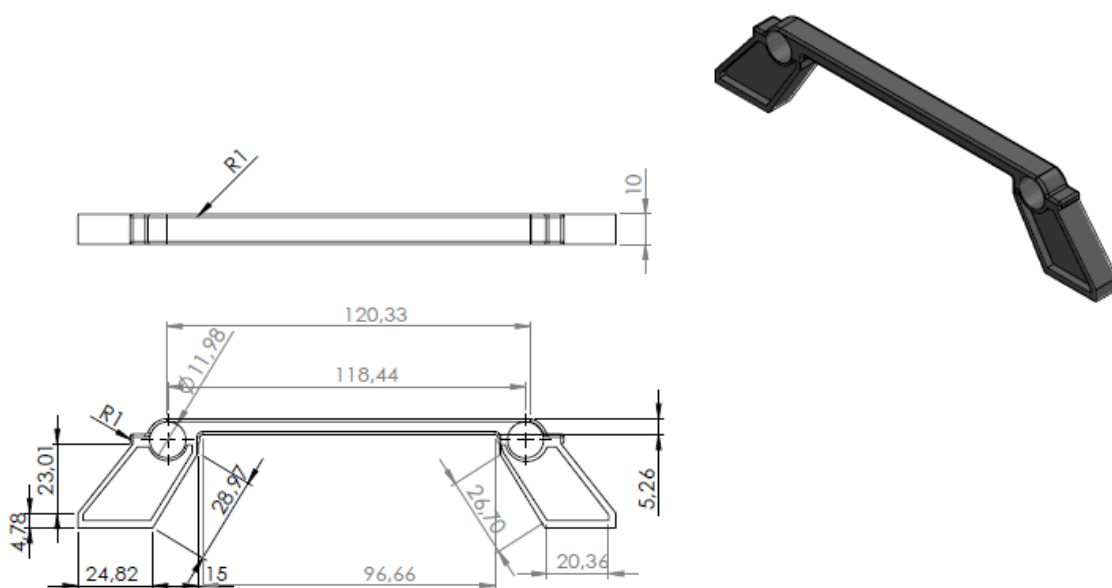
3D модель креплений баз гексакоптера в SolidWorks
